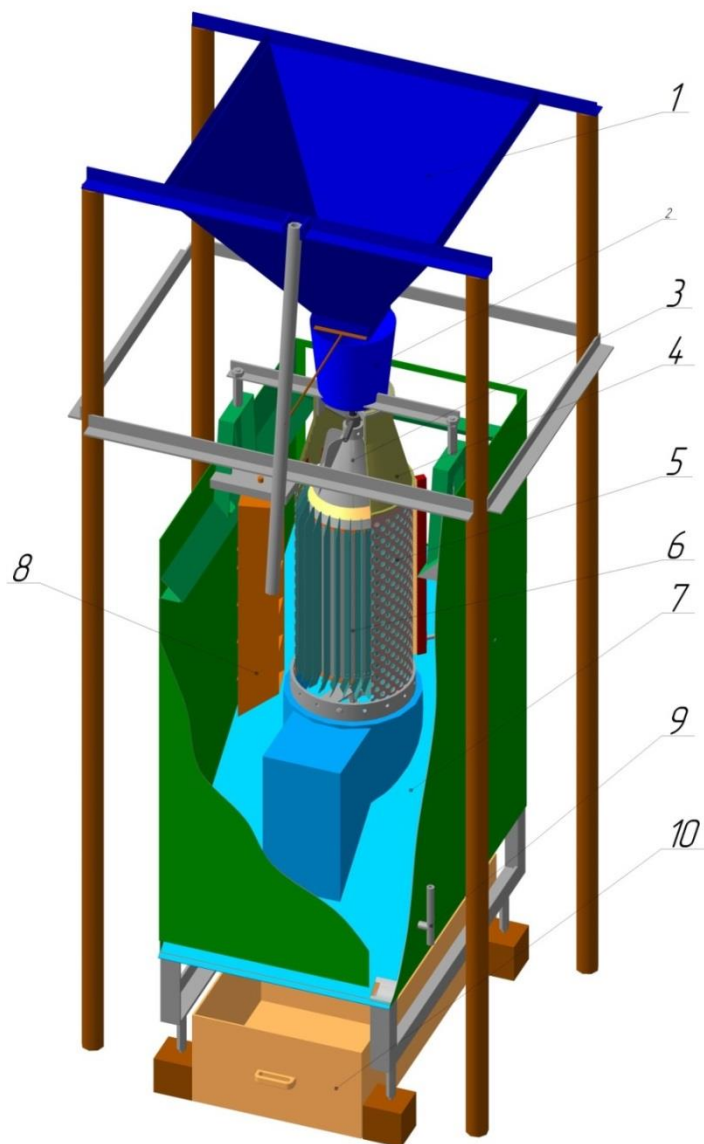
3D- модель лабораторной установки центробежно-решетного сепаратора с подсевным решетом:
